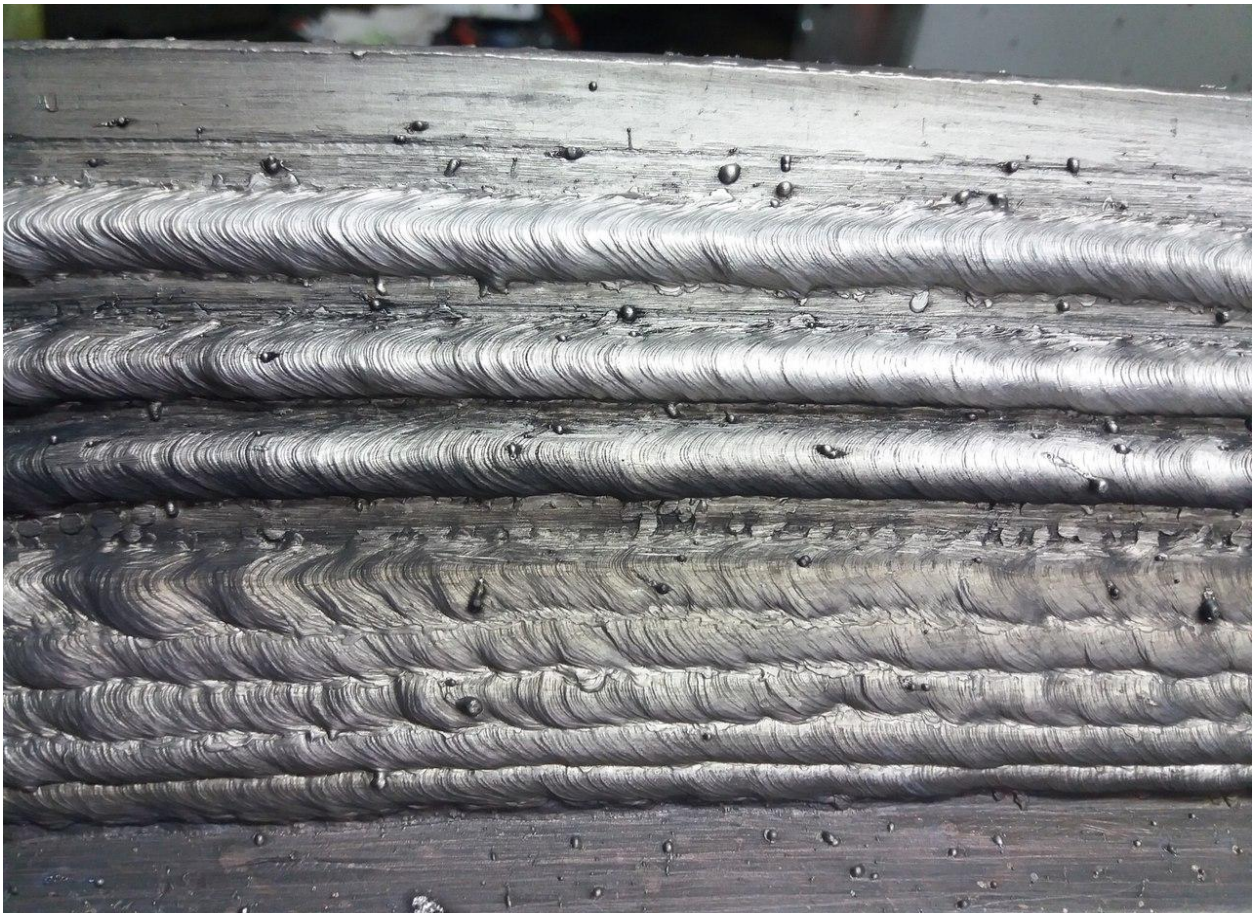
Наплавленная поверхность внутренней части уплотнительного кольца
